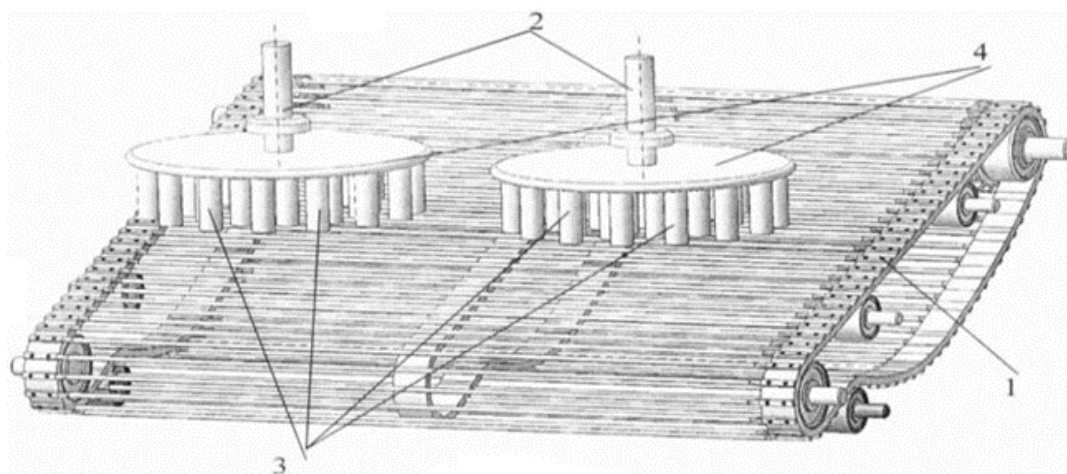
Пальчатый интенсификатор, расположенный над поверхностью элеватора:
